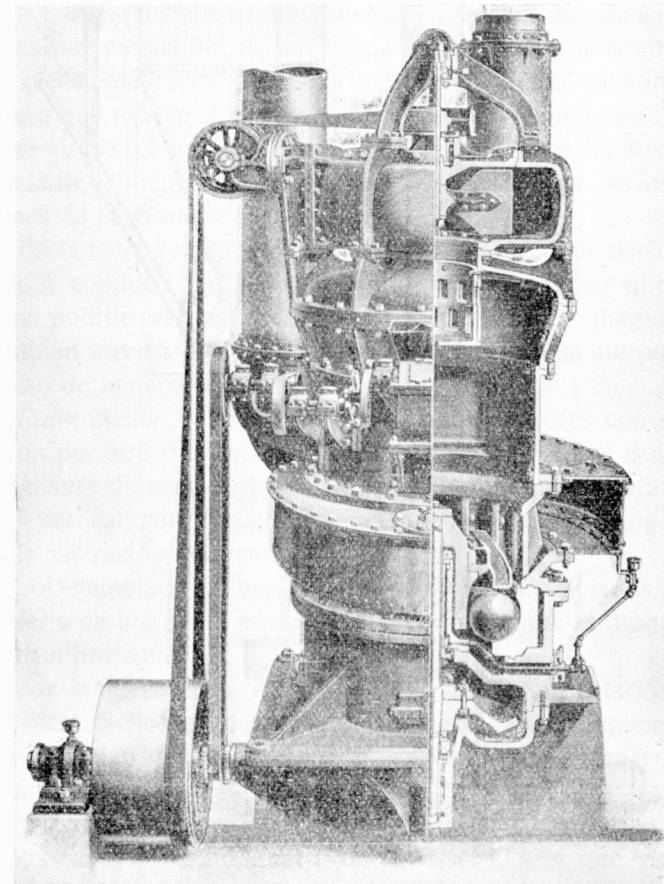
Pulverizador Fuller-Lehigh con separación por aire.
